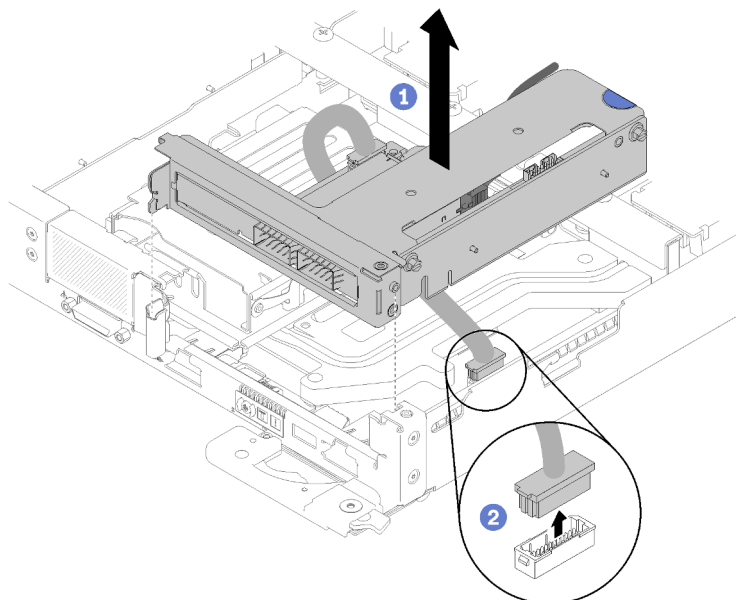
Entfernen der Gehäusebaugruppe für PCIe-Adapterkarte
